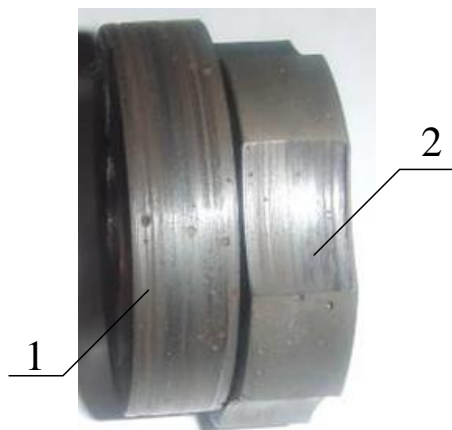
Внешний вид поверхностей трения образцов «Металлополимер –Metalлополимер»
